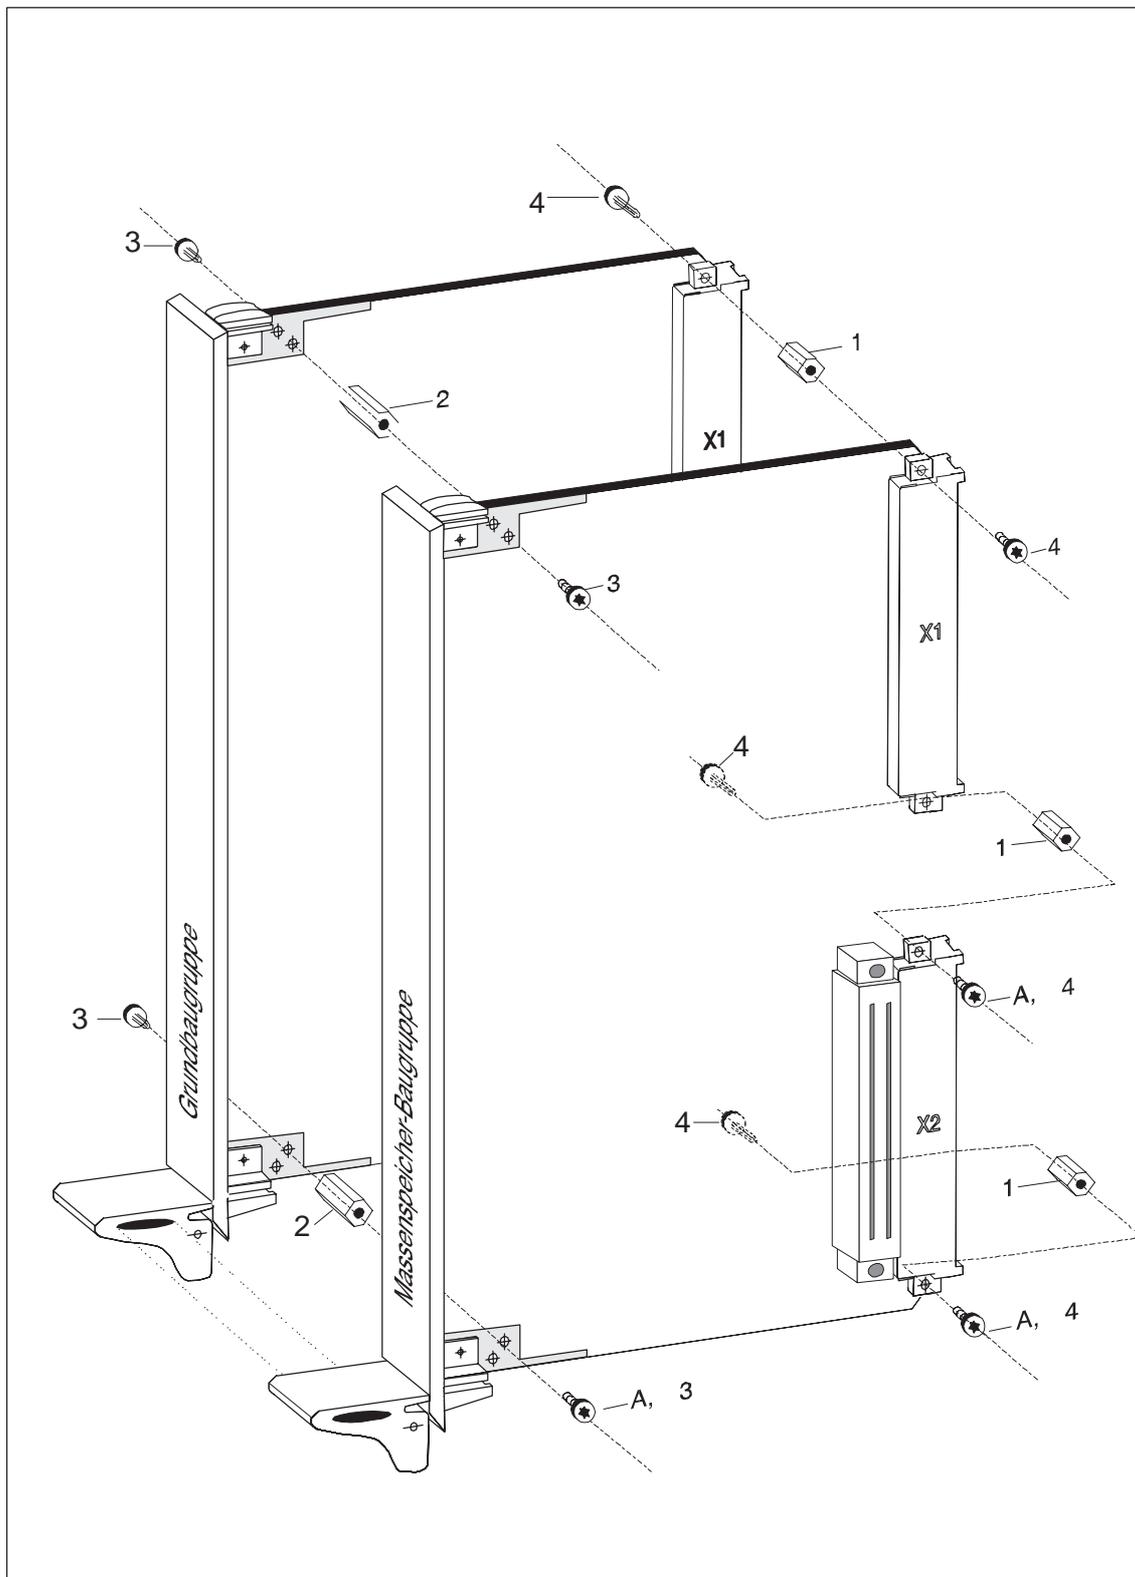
Montage der Massenspeicher-Baugruppe auf der Grundbaugruppe
